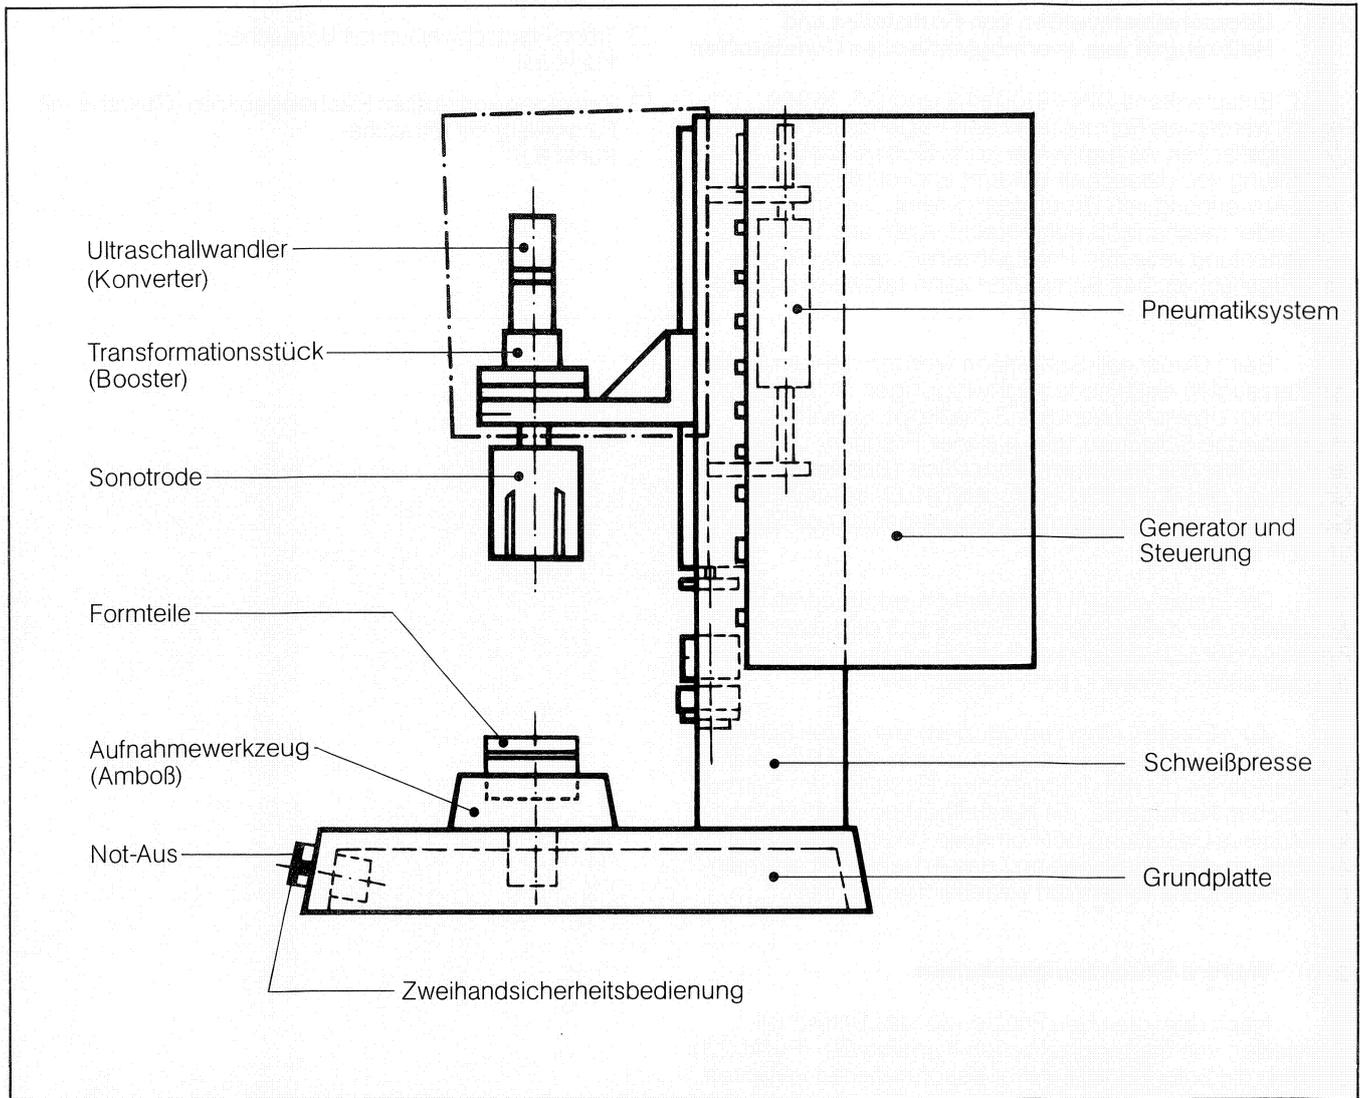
Schematischer Aufbau eines Ultraschall-Schweißgerätes
